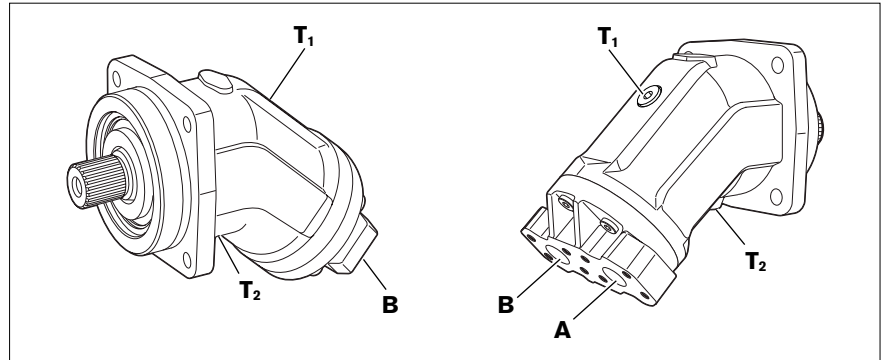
Vue d'ensemble des raccords A2FM, raccords de service à l'arrière
